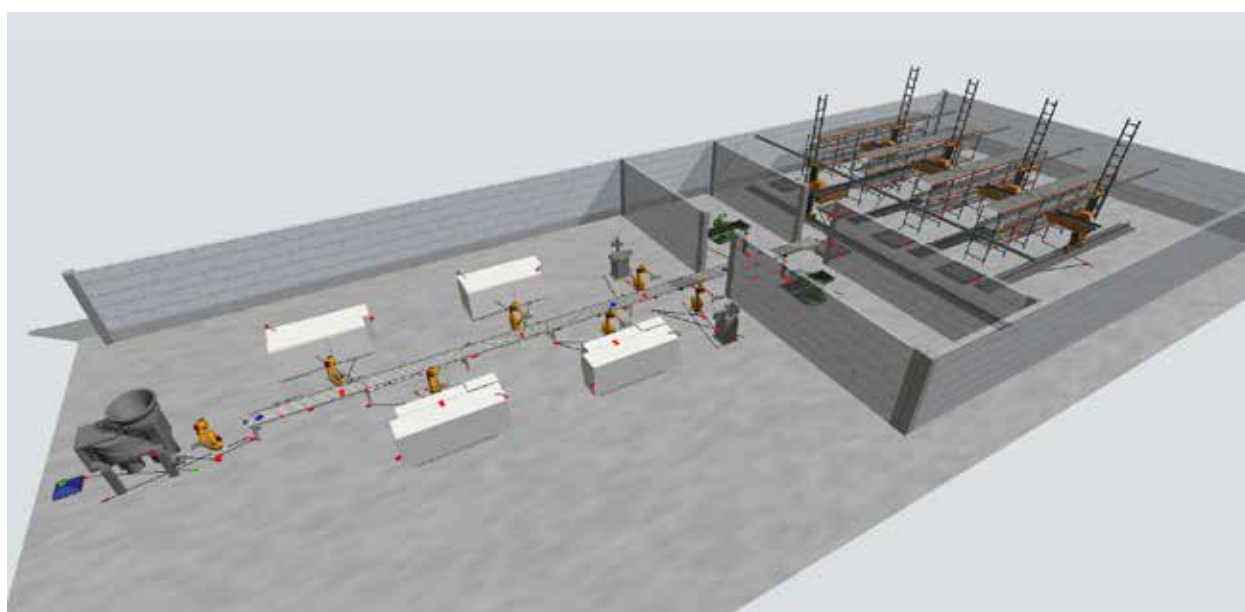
Цифровий двійник виготовлення деталі типу фланець
